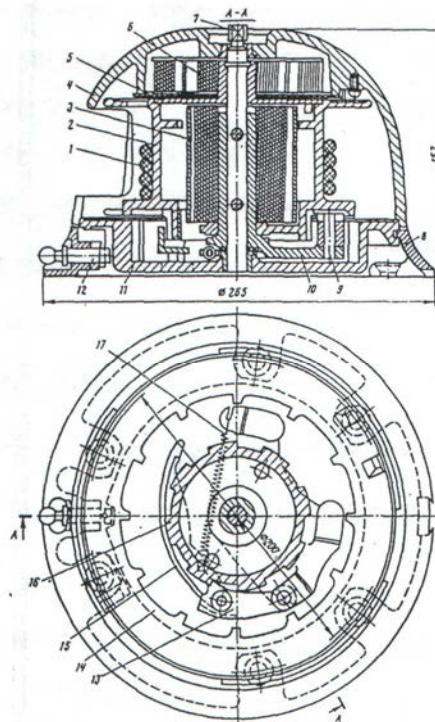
Механический штангоуловитель: 1 – канатик; 2 – барабан; 3 – главная пружина; 4 – крышка; 5 – втулка фланца; 6 – вспомогательная пружина; 7 – квадрат для рукоятки; 8 – держатель; 9 – ось; 10 – поводок; 11 – храповик-тарелка; 12 – штифт; 13 – главная защелка; 14 – храповик; 15 – отключающая защелка; 16 – храповик отключающей защелки; 17 – пружина защелки
